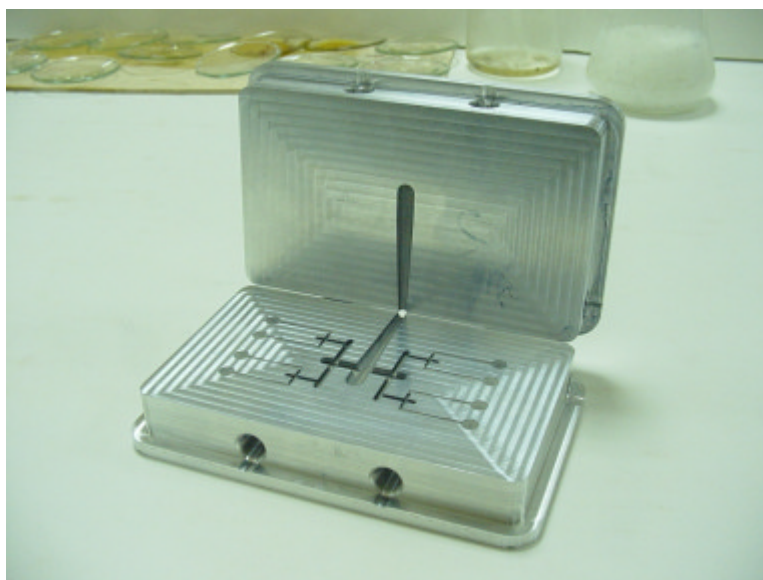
Impressões em duroaluminio obtidas por *Laser Milling
